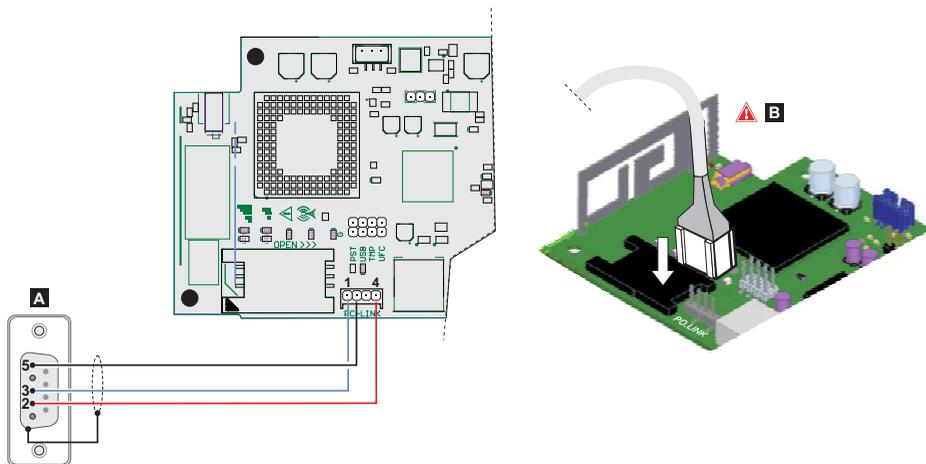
Connexion par câble PC-Link : A) Connecteur RS-232 femelle, côté soudure B) Insérer correctement le câble PC-Link.
